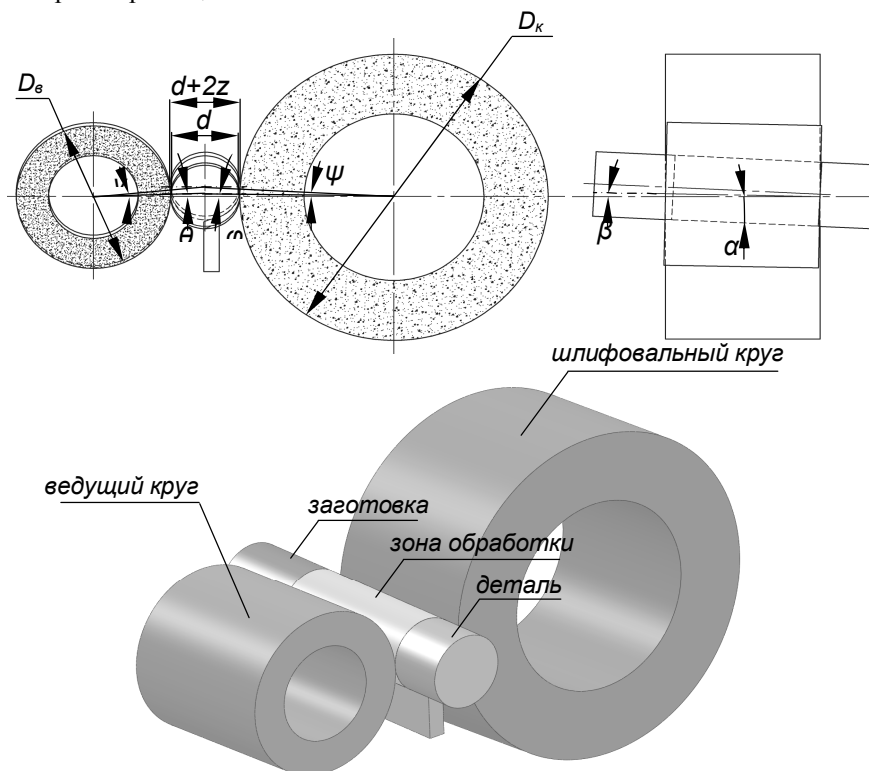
Схема бесцентрового шлифования со скрецающимися осями инструмента и детали
